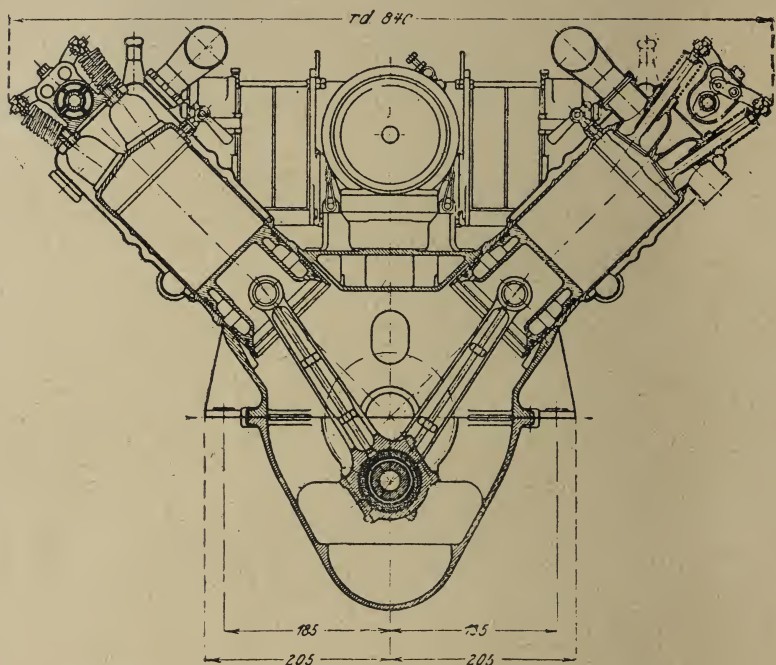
Achtzylinder-V-Schnelläufer von Gebr. Körting. Querschnitt.
